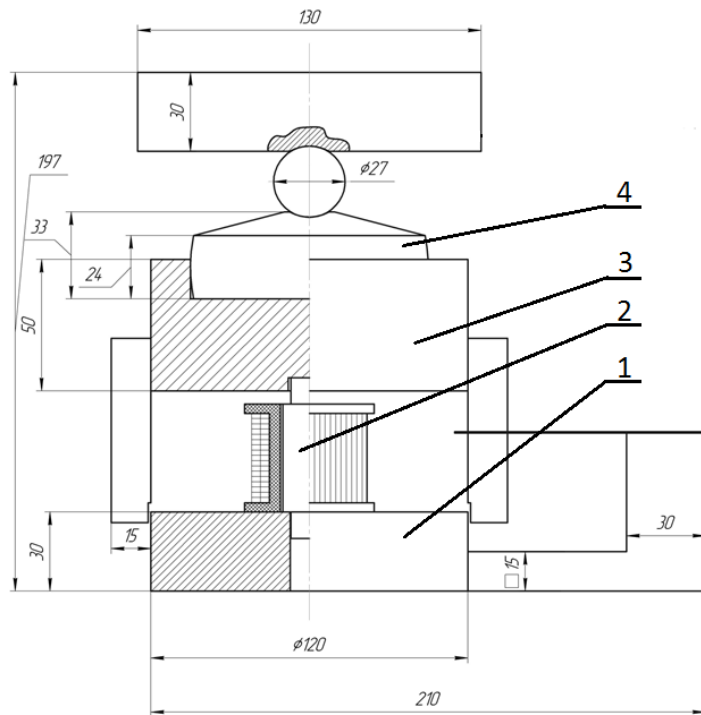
Общий вид установки для исследования силы срыва посадки с натягом с зазором в магнитопроводах (пластины по сторонам)
